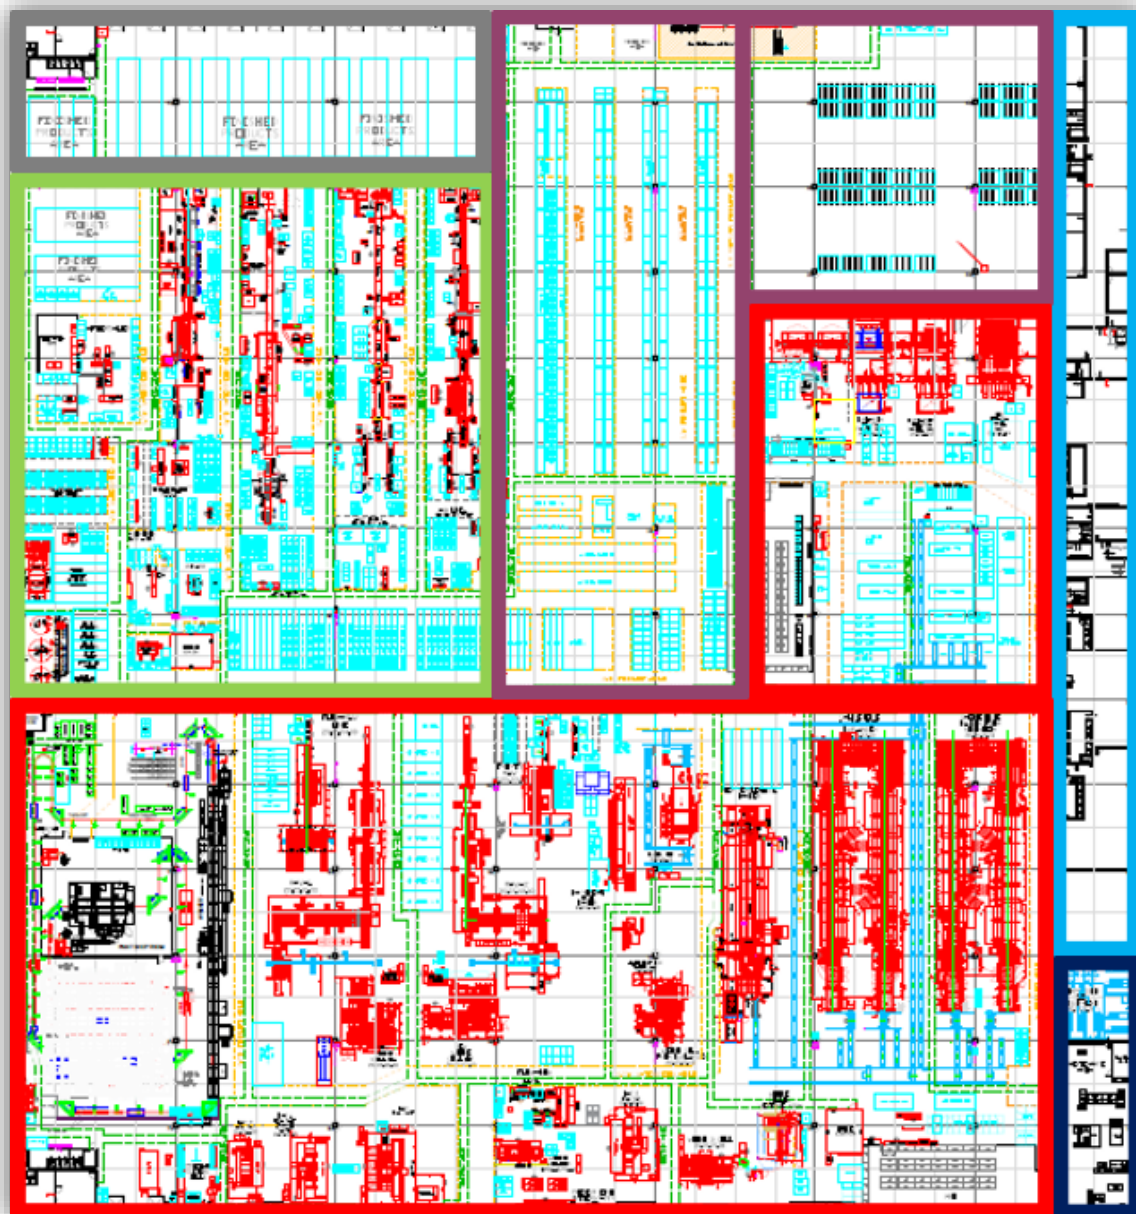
Layout výrobního závodu Steelcase Czech Republic s. r. o.
